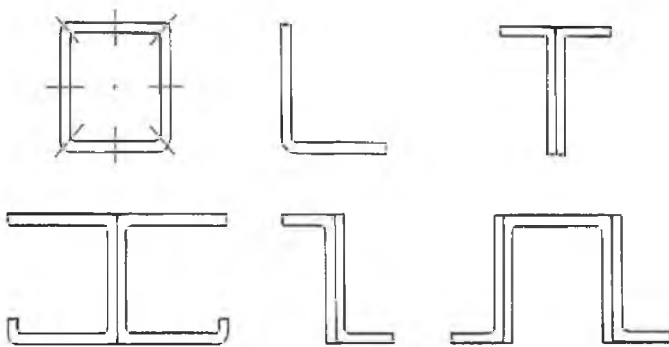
Варианты изготовления шпангоутов последующей разрезкой коробчатой конструкции и склеиванием ее элементов
